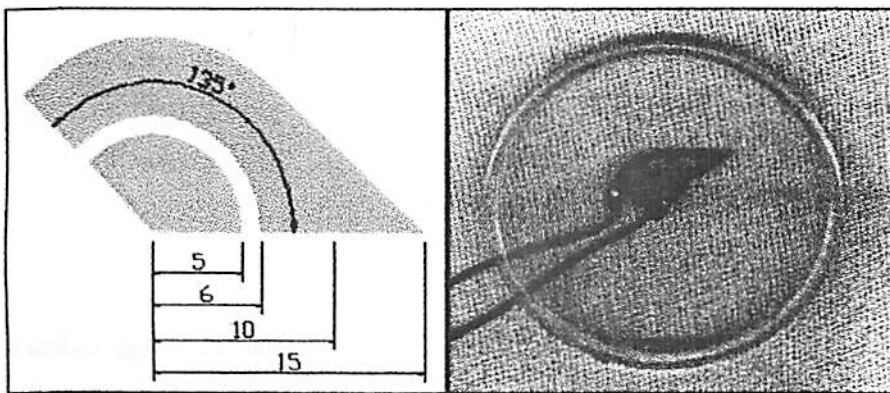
Detalhes das pistas e montagem sob a tampa do vacuômetro de Bourdon, medidas em mm.
